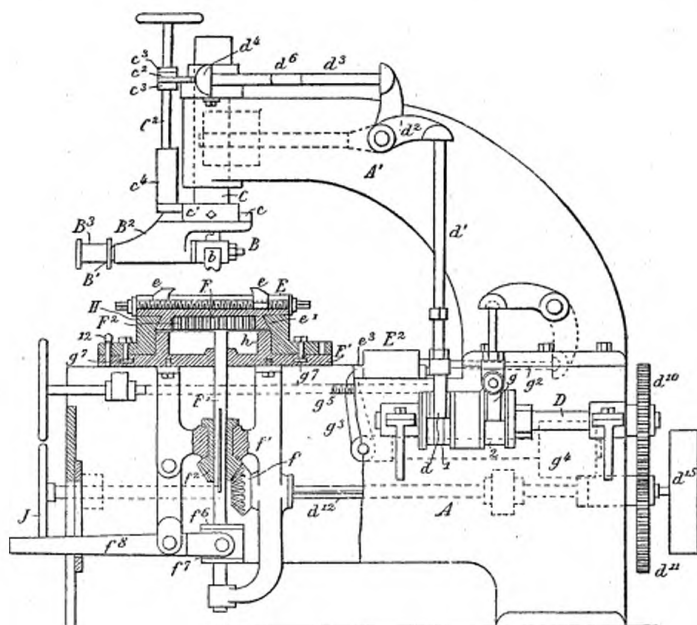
Machine Van Houten à faire les moulures, ornements et dessins divers.
